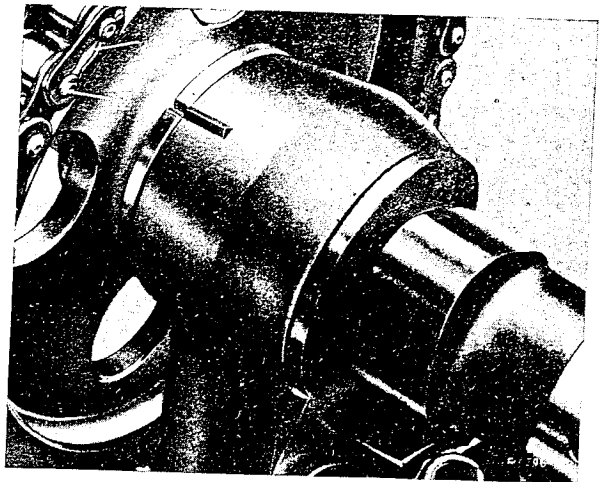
Die Strichmarken auf der Ausgleichsscheibe und dem Nockenwellenlager sind gefluchtet (OM 621)
